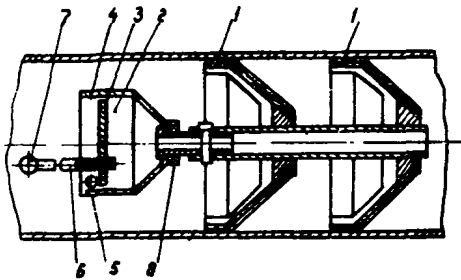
Гидродинамическое очистное устройство с приспособлением для его поиска
